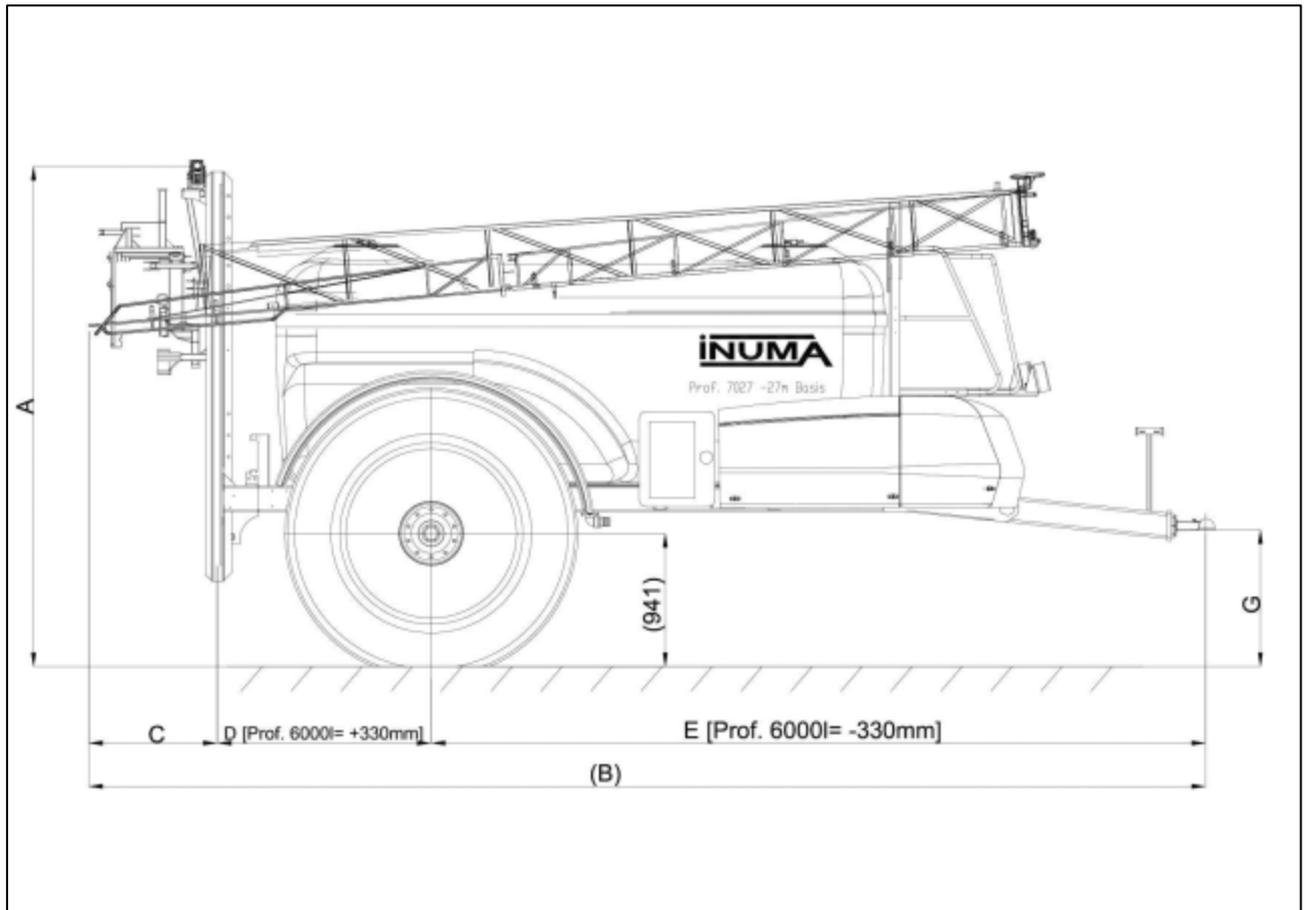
Abmessungen Anhängerspritze Gestänge 27 m Basis - 6000 / 7000 I
